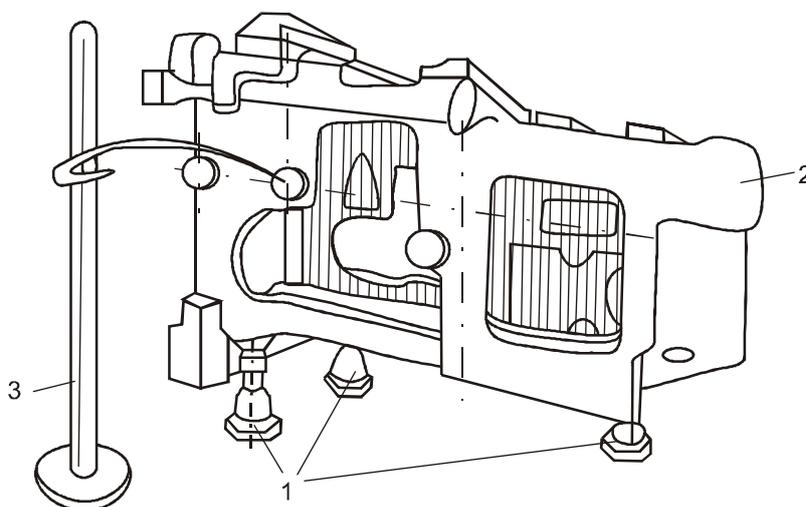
Схема выверки заготовки корпусной детали по проверочной установочной базе:
